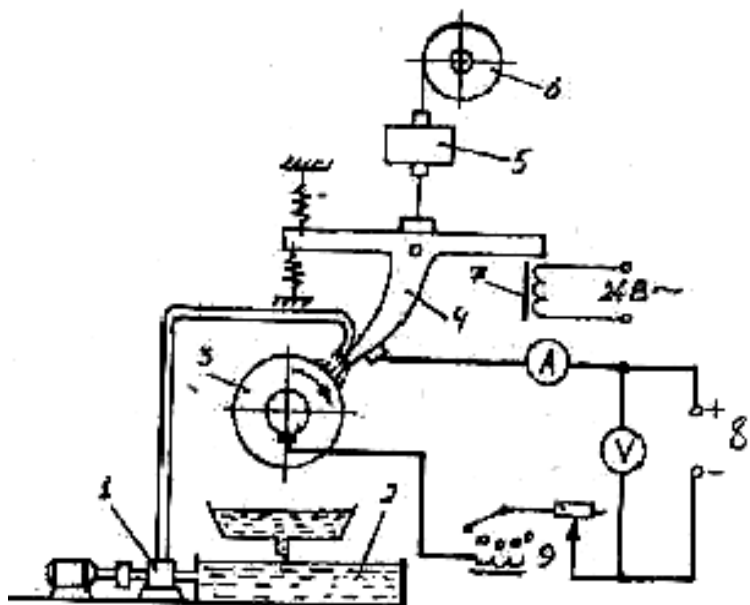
Схема установки для вибродуговой наплавки: 1 – насос; 2 – поддон; 3 – наплавляемая деталь; 4 – мундштук; 5 – механизм подачи электродной проволоки; 6 – кассета с электродной проволокой; 7 – электровибратор; 8 – источник тока; 9 – дроссель
